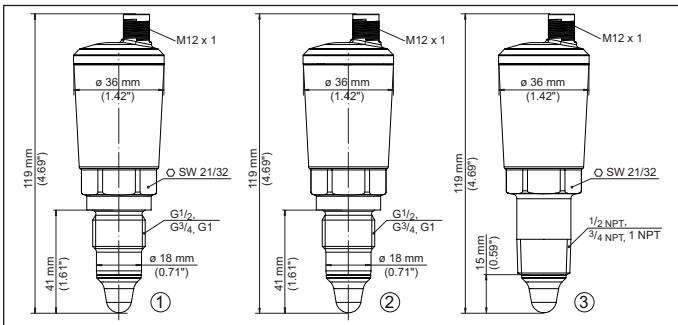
VEGAPOINT 21, Standardausführung - Gewinde mit M12 x 1-Stecker
